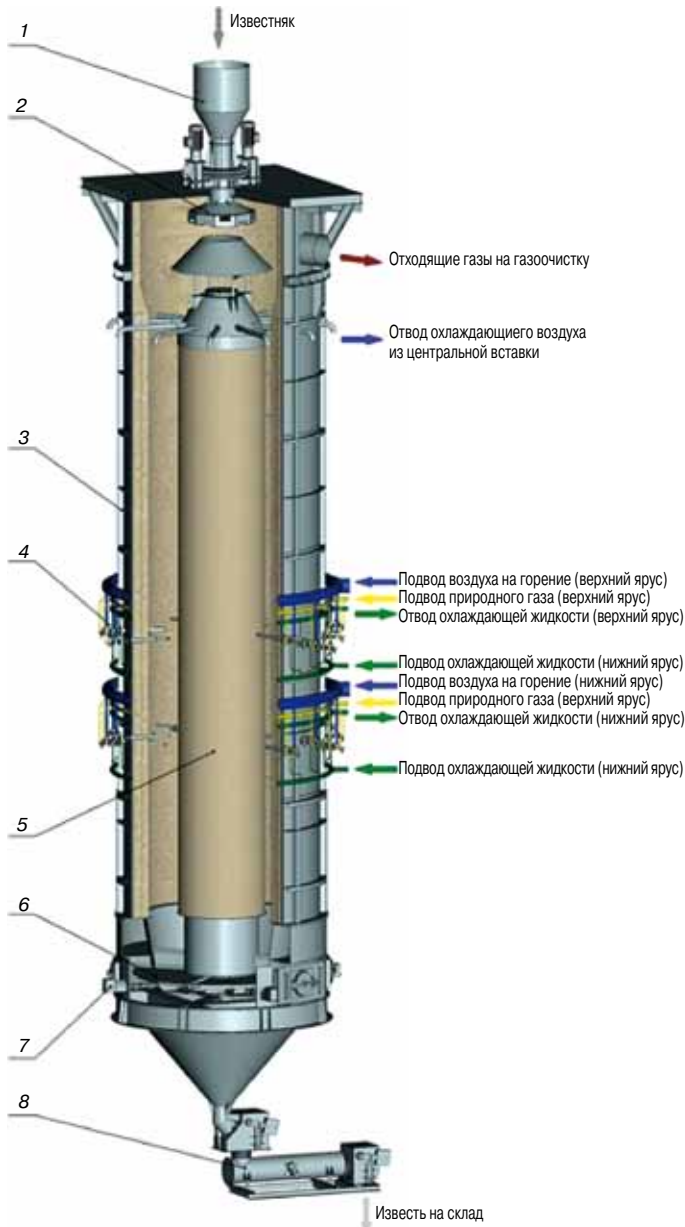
Общий вид противоточной шахтной кольцевой печи для получения мягкообожженной извести: 1 – бункер загрузочный; 2 – питатель тарельчатый; 3 – корпус печи; 4 – формы периферийные; 5 – вставка огнеупорная; 6 – стол выгрузочный секторный; 7 – гидроцилиндры привода выгрузочного стола; 8 – тамбурная система выгрузки
